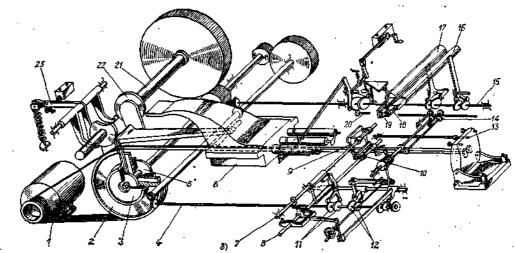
Кинематическая схема автомата для горячей штамповки коротких изделий
